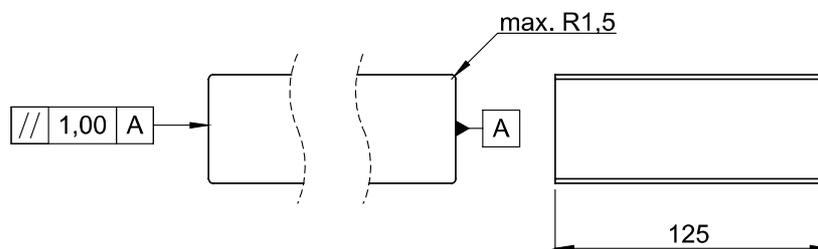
Requisitos que debe cumplir la pieza de trabajo
